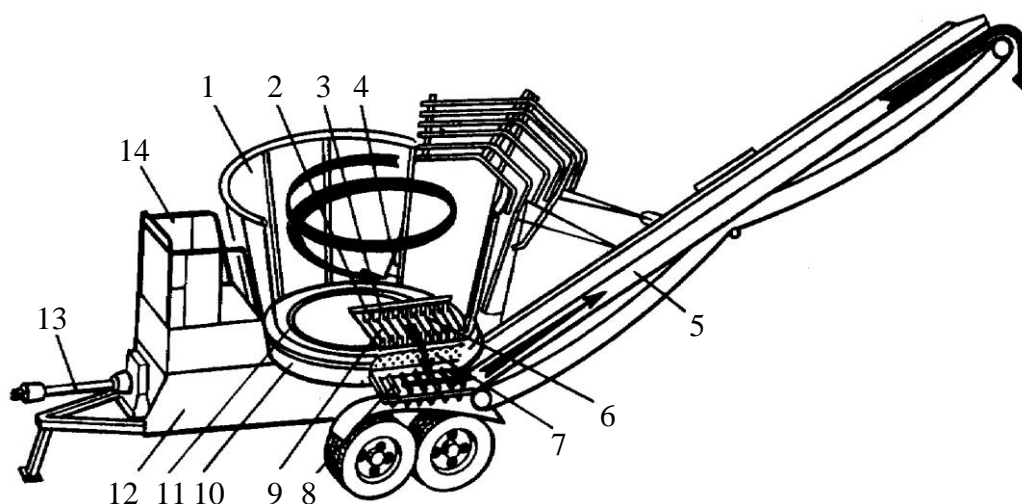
Схема дробилки-измельчителя ИРТ-165:
